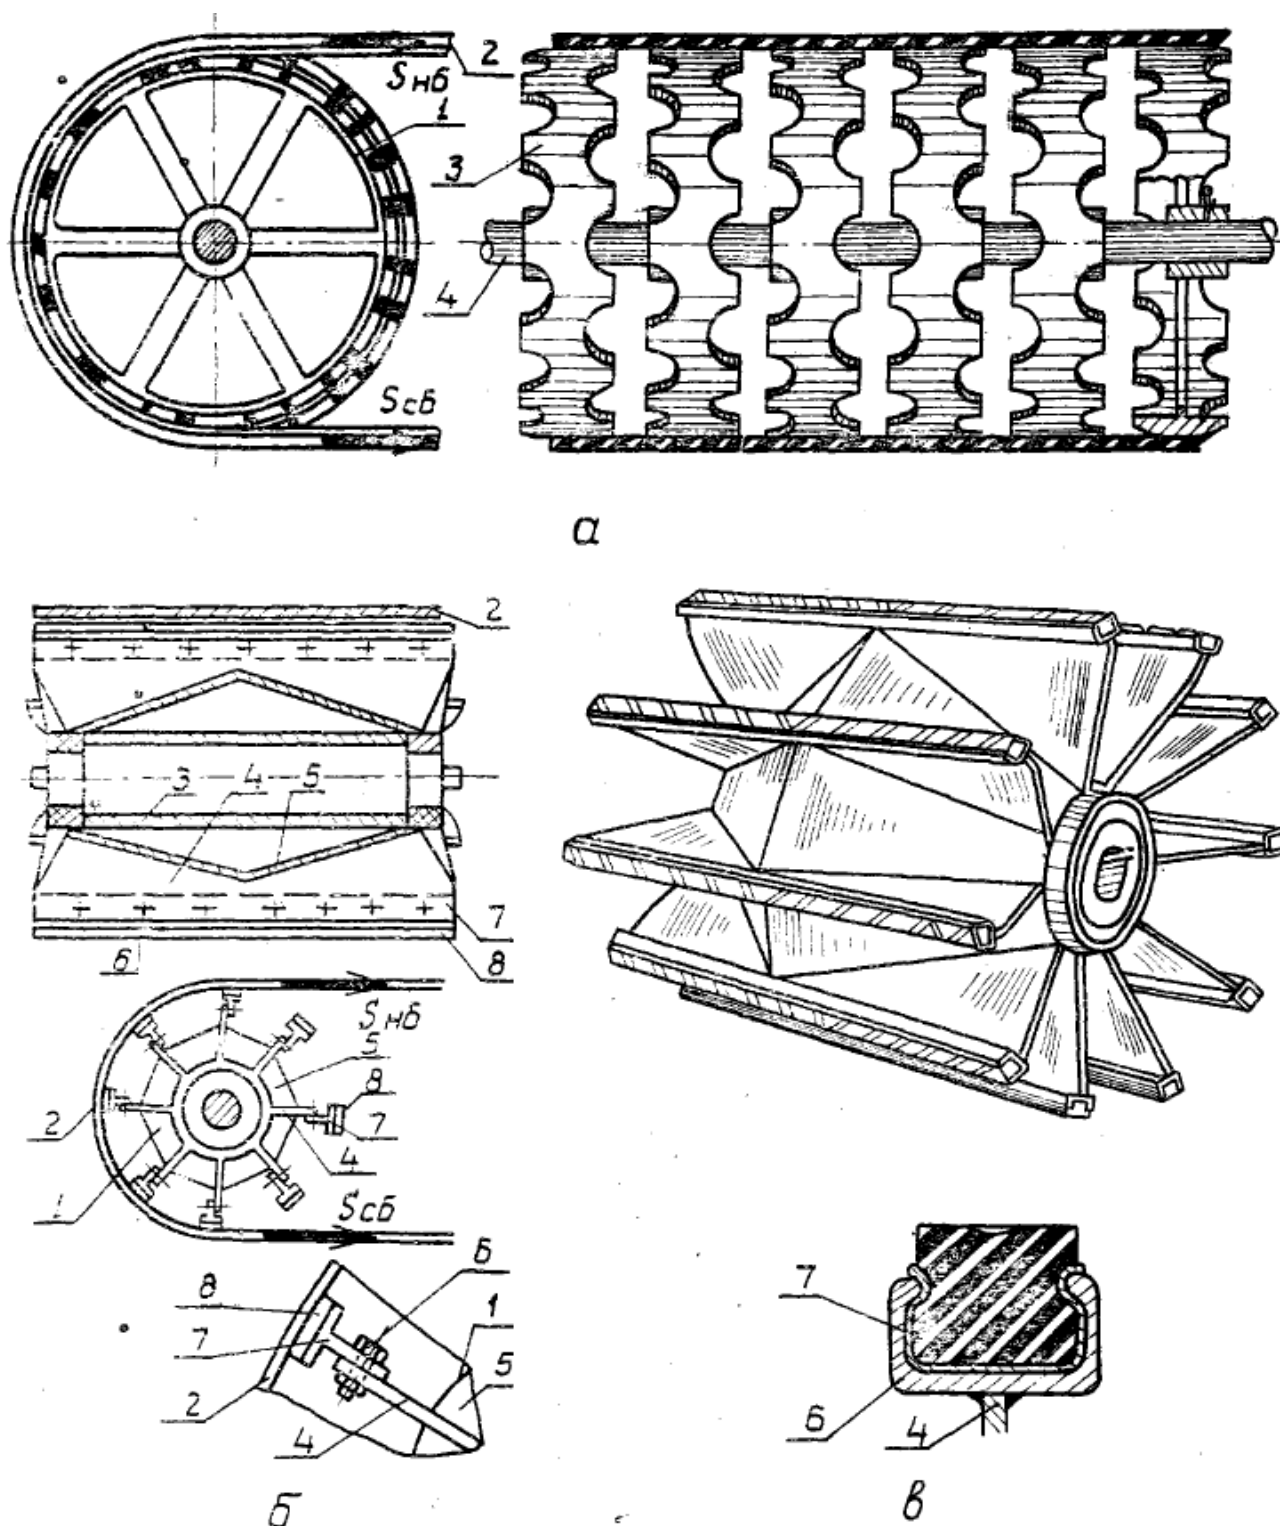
Схеми приводів з приводними барабанами, що самоочищуються: а - схема привода з нефутерованим барабаном, що самоочищується; б - схема привода з лопатевим барабаном, що самоочищується; в - конструкція футерованого ребристого барабану, що самоочищується
